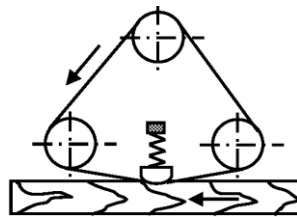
Схема широкострічкового шліфувального верстата
